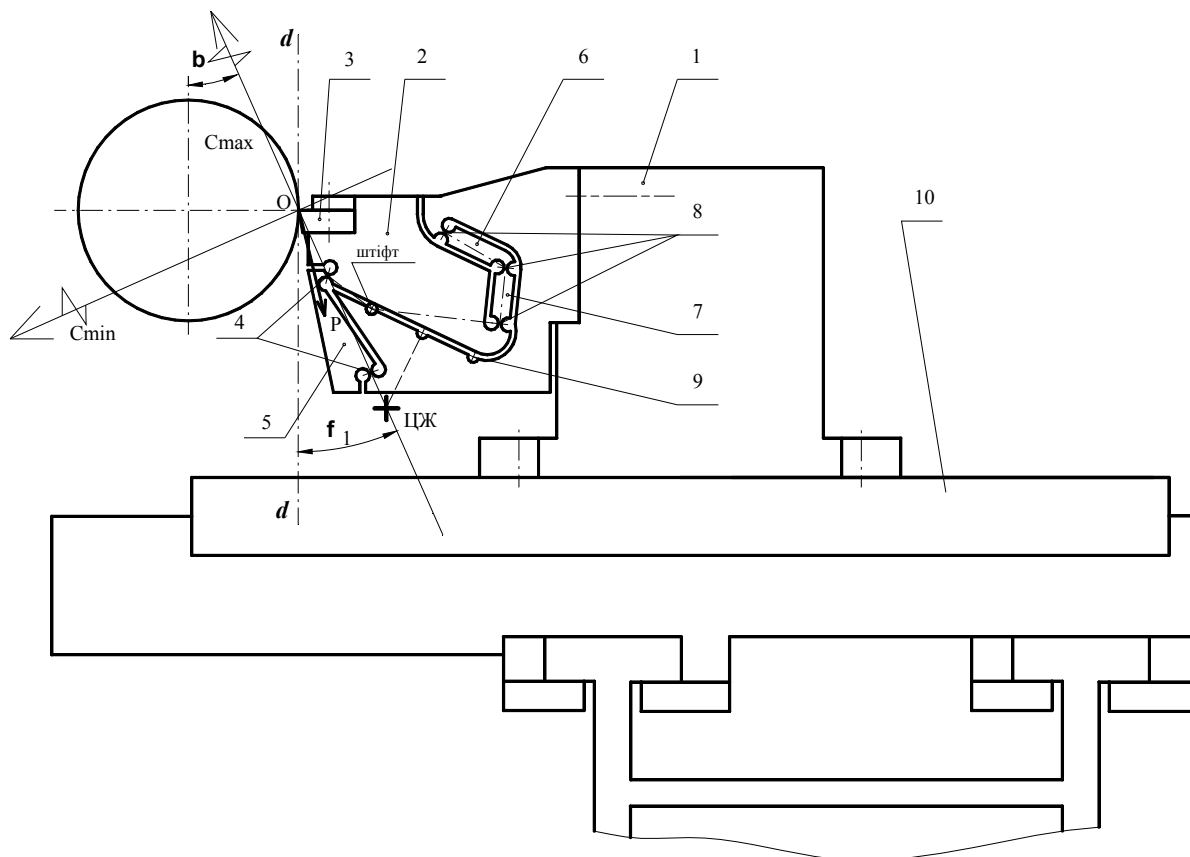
Схема конструкции токарного резцедержателя с регулируемым положением центра жесткости
